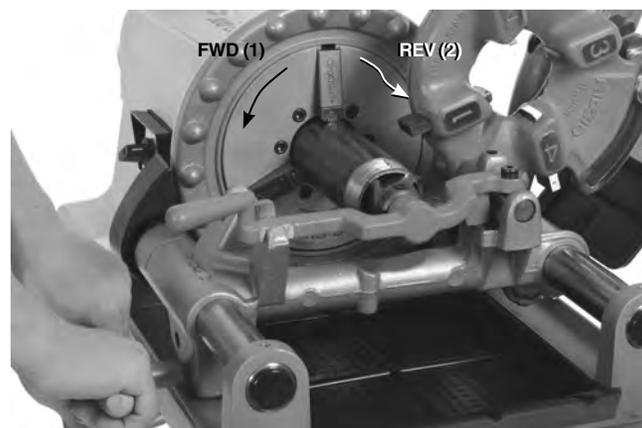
Fräsen des Rohrs mit dem Innenrohrfräser, Maschinenrotation
